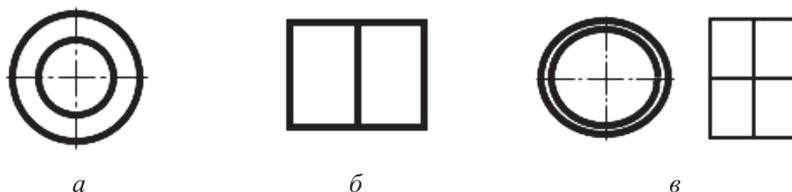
Типы образцов с остаточными сварочными напряжениями:
